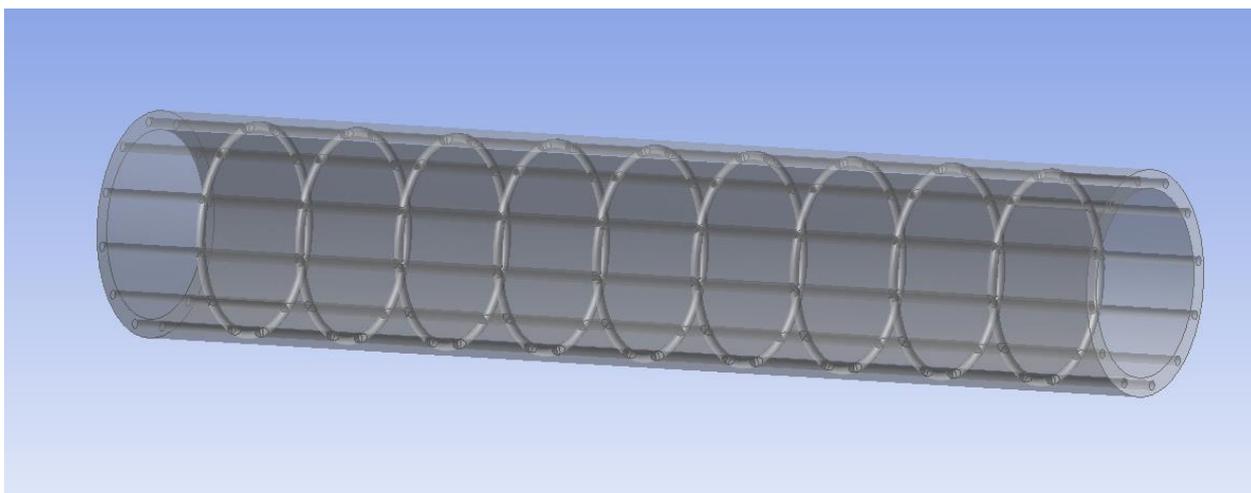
Модель алюминиевой матрицы композитной трубы.
